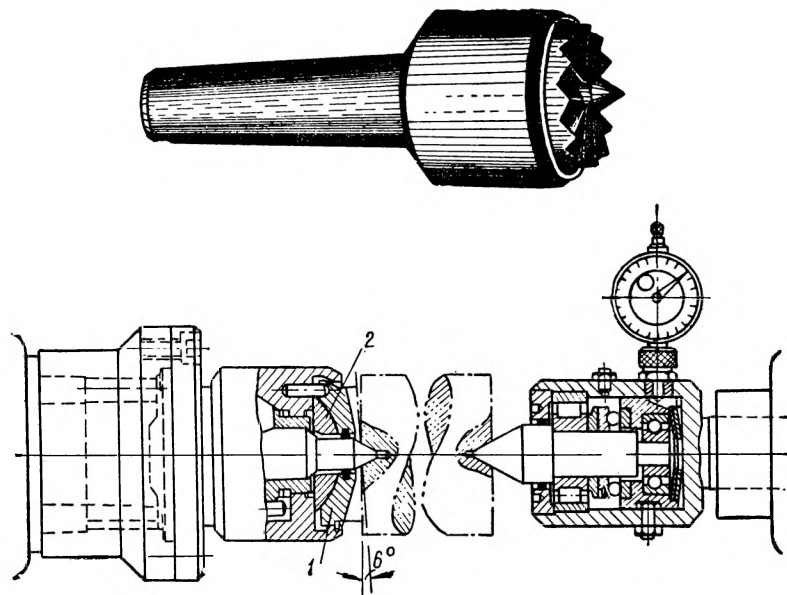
Специальный центр для установки детали с неподрезанным торцом.
